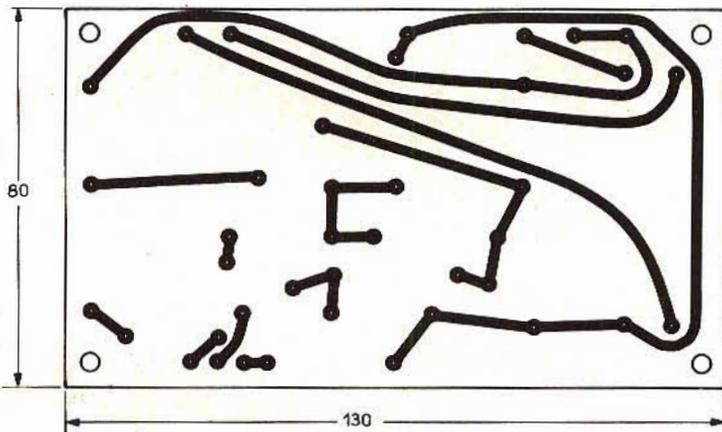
Disegno illustrante la traccia del circuito stampato, le cui dimensioni devono essere di circa 130 x 80 mm.
